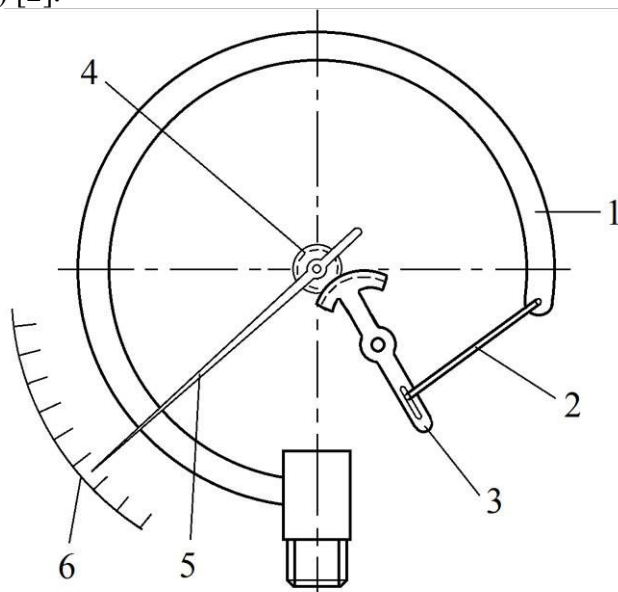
Схема манометра с трубчатой пружиной и передаточным механизмом в виде зубчатого сектора: 1 - трубчатая пружина (трубка Бурдона); 2 – тяга (поводок); 3 - зубчатый сектор; 4 – зубчатое колесо (трибка); 5 – стрелка; 6 - шкала
